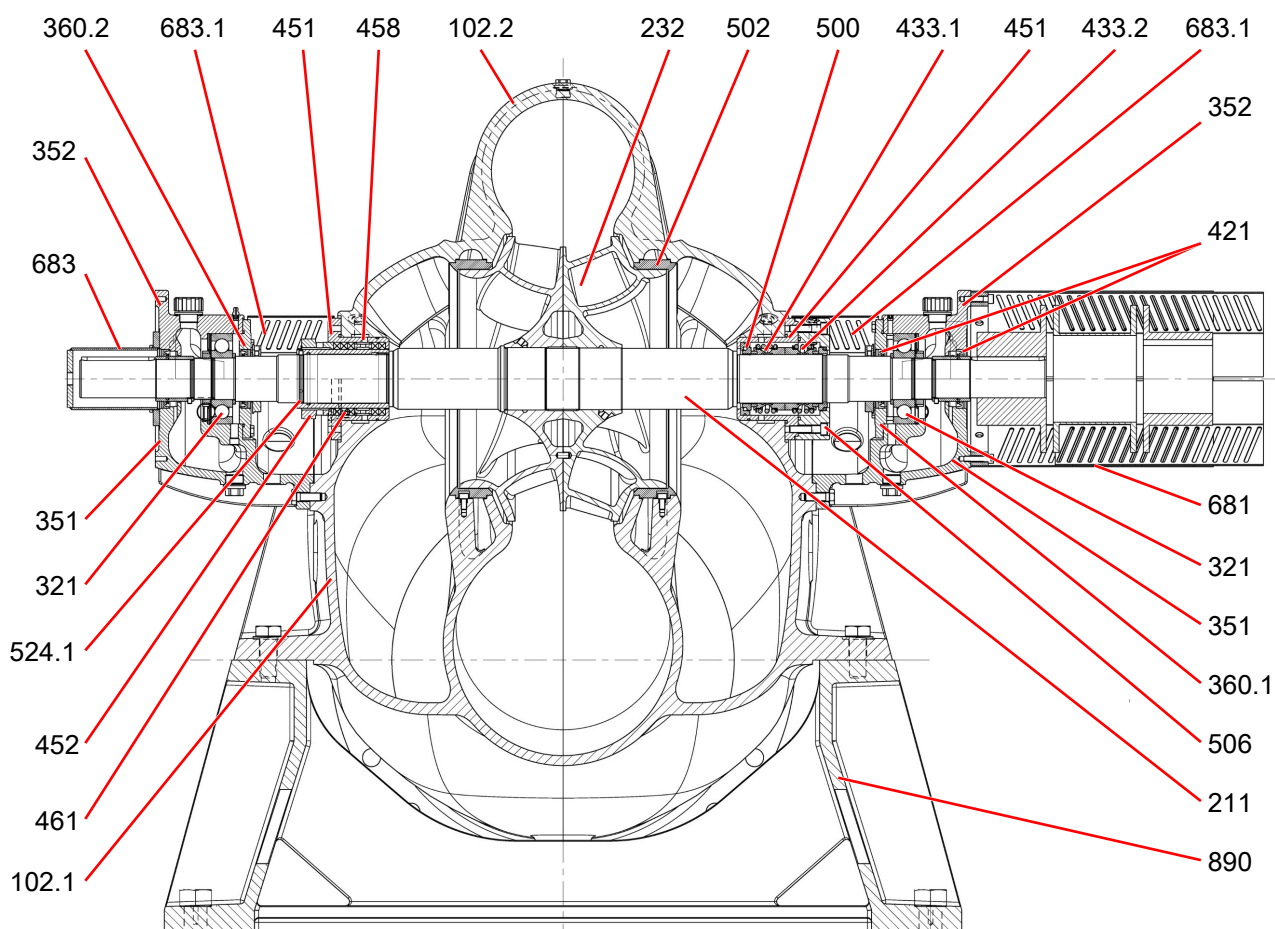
Чертеж насоса ASP-R.P.S в разрезе (соосные лопасти рабочего колеса, платформа, прессовая посадка)
